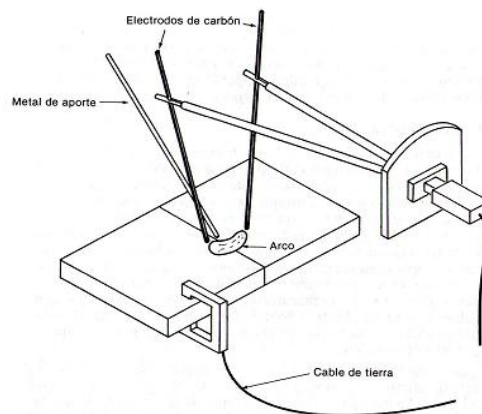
Disposición de los elementos para soldadura de arco con carbones gemelos.
